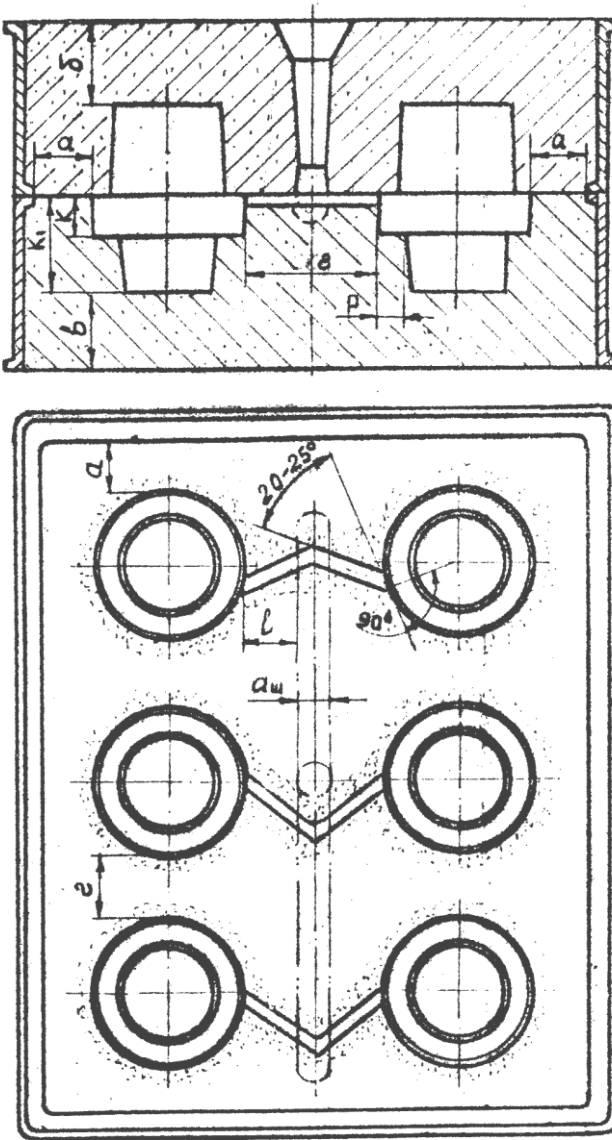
Схема розташування виливків у ливарній формі
